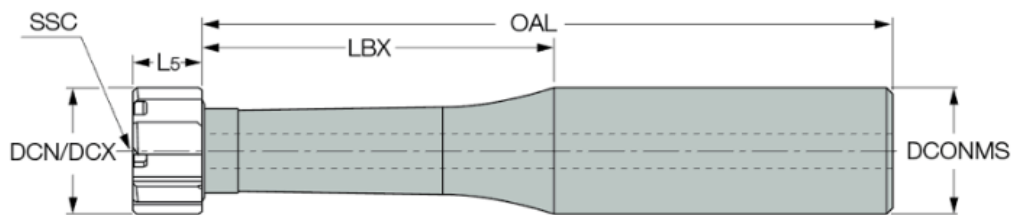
Monolitní fréza ze slinutého karbidu ECR-B3-R-C [52].
